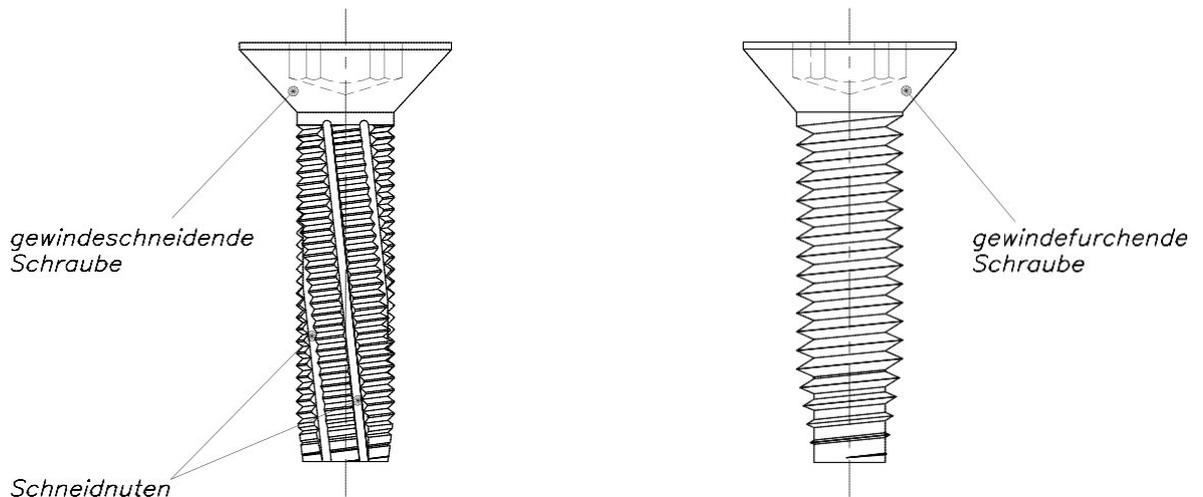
Gewindeschneidende und gewindefurchende Schrauben
